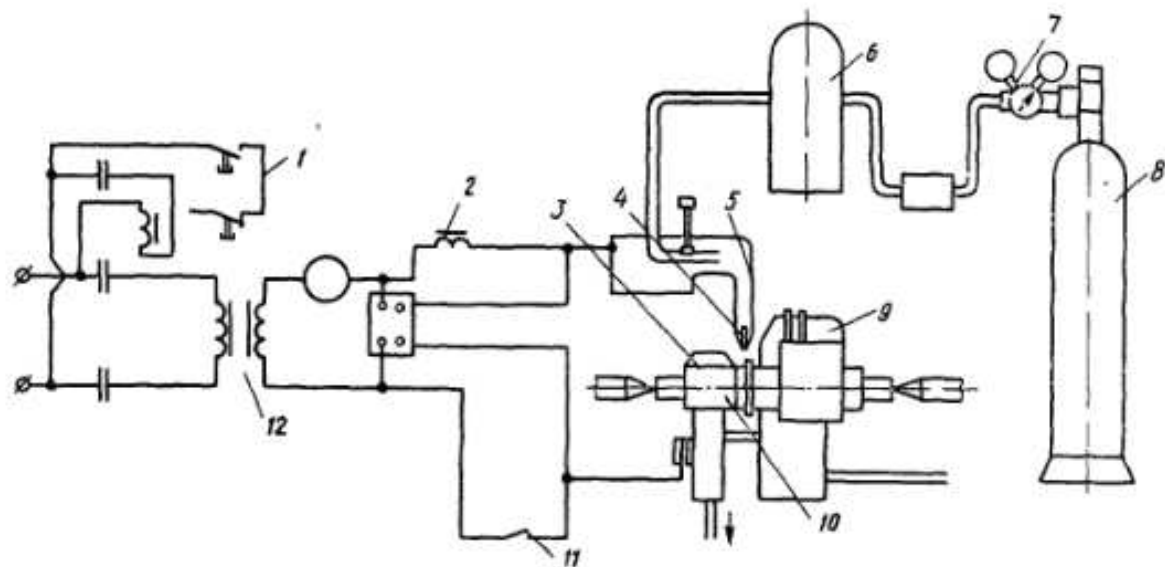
Принципиальная схема установки для аргоно-дуговой сварки концов секций с петушками коллектора
